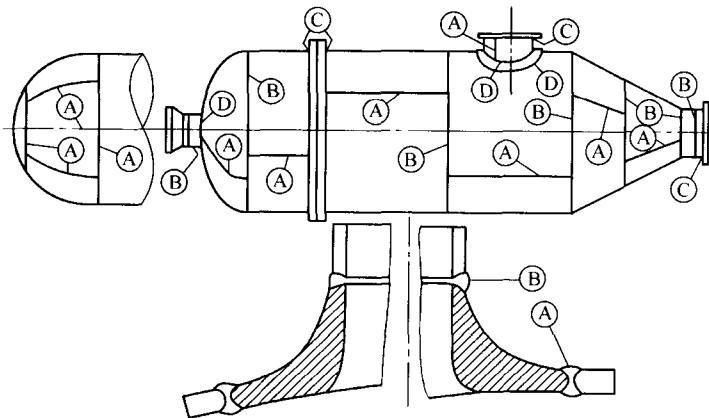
压力容器焊接接头形式分类示意图
